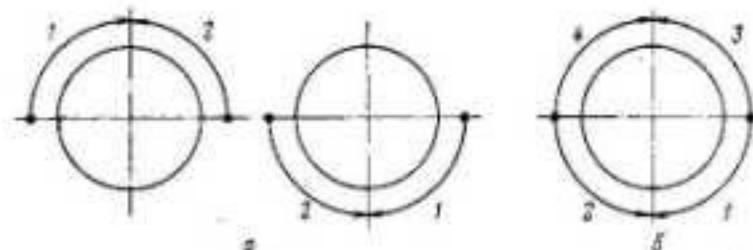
Последовательность сварки первого слоя при выполнении сварки за два поворота:
